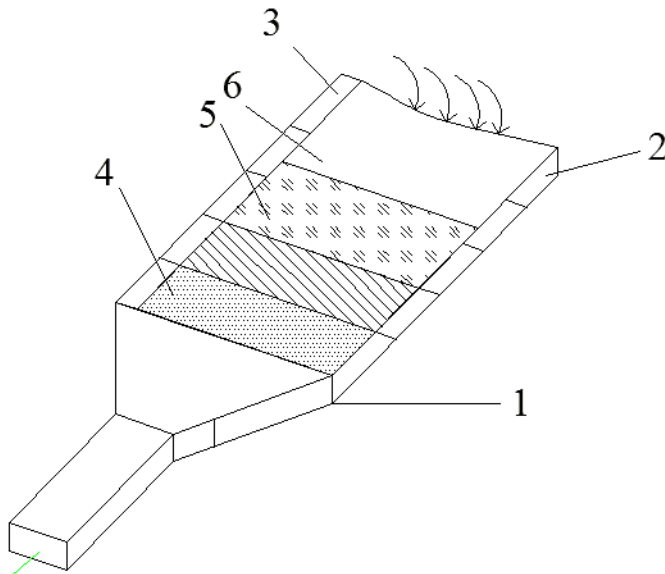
Пластийний плівковий сонячний повітропідігрівач: 1-корпус, 2,3-корпусні деталі; 4-решітчастий тримач; 5-поглинаюча плівка; 6-світлопрозора плівка.
